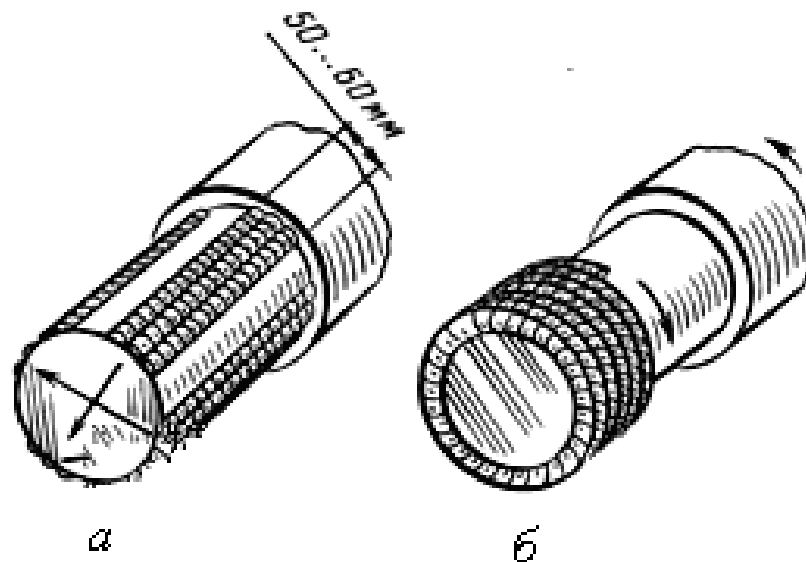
Последовательность наплавки валиков при восстановлении изношенной поверхности вала: *а* — ручным способом; *б* — механизированным способом, 1... 5 - последовательность наплавки.
